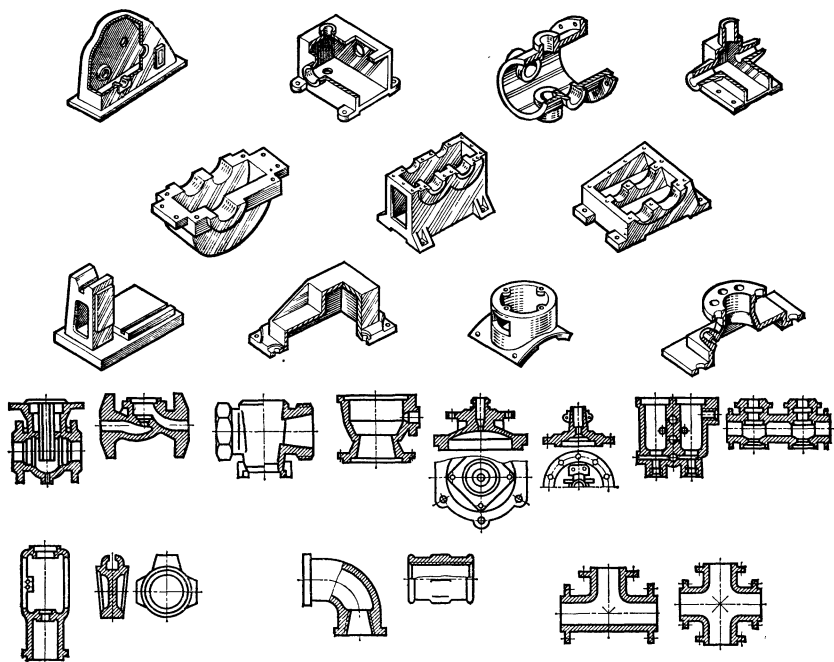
Укрупненный классификатор деталей арматуры и корпусных деталей
